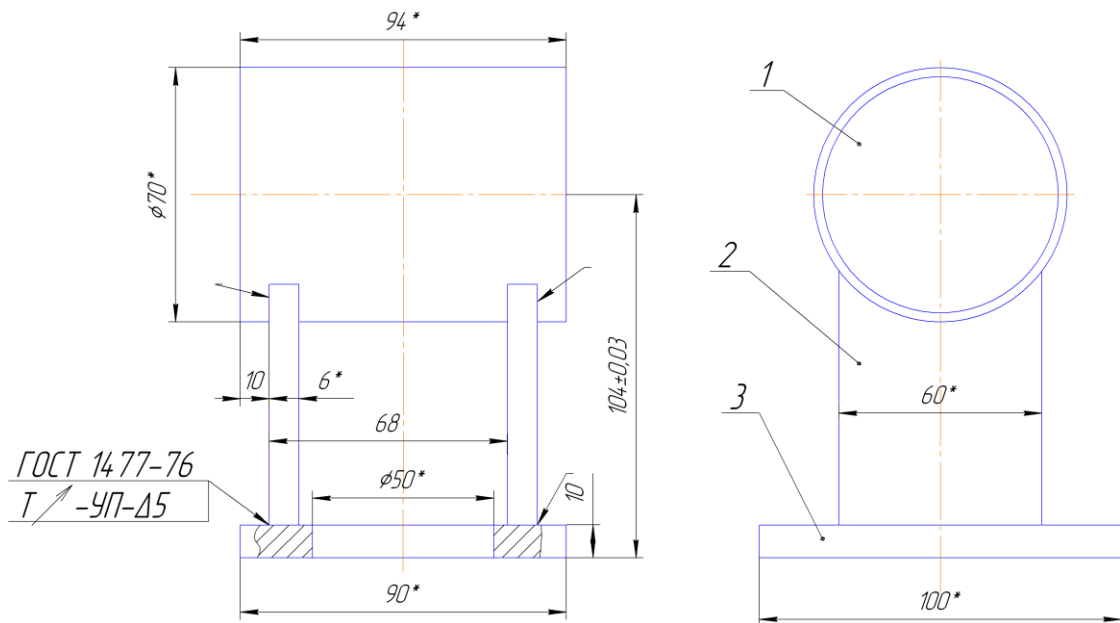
Ескіз обробки елементу деталі з виливка
